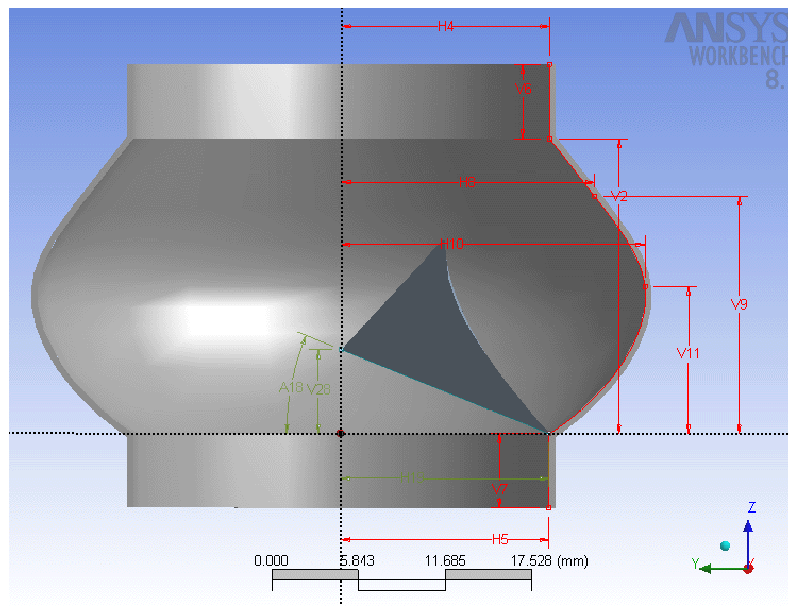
Posicionamento da reta de construção do folheto, dentro da parede da válvula.
